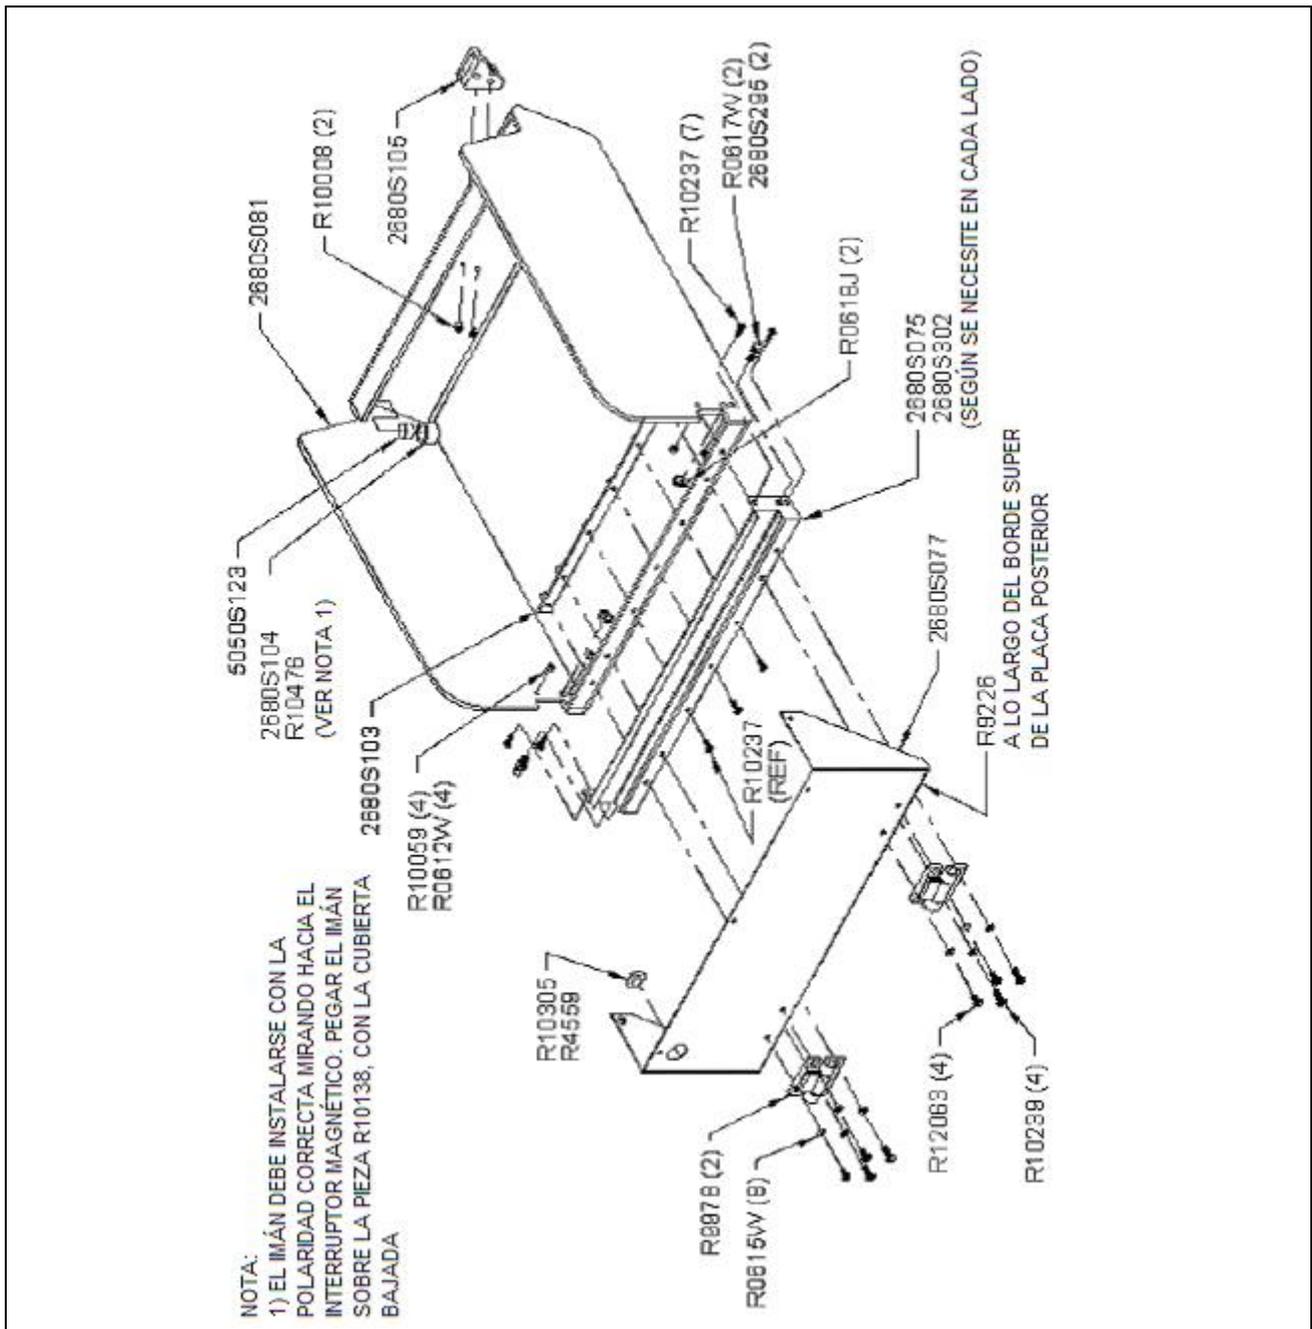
Dibujo de despiece de la cubierta de la máquina (2680S802).
